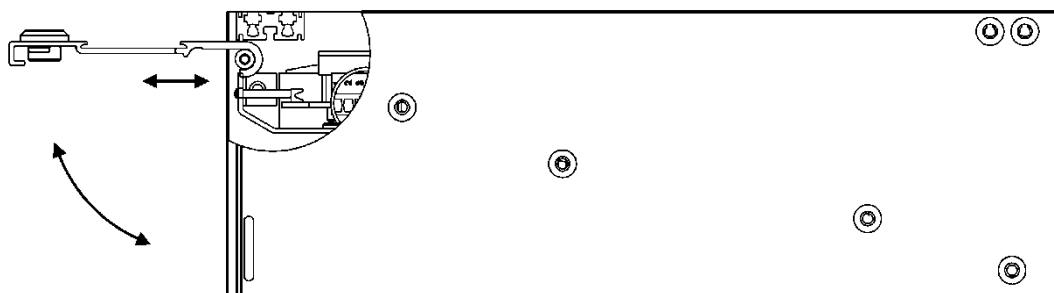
Seitenansicht mit geöffneter schwenkbaren Frontabdeckung
